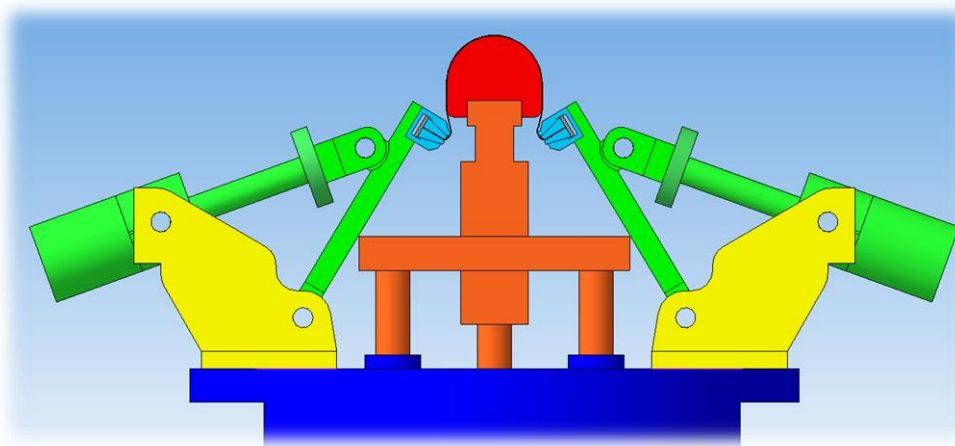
Схема лабораторного обтяжного пресса (конечное положение рабочих органов)
